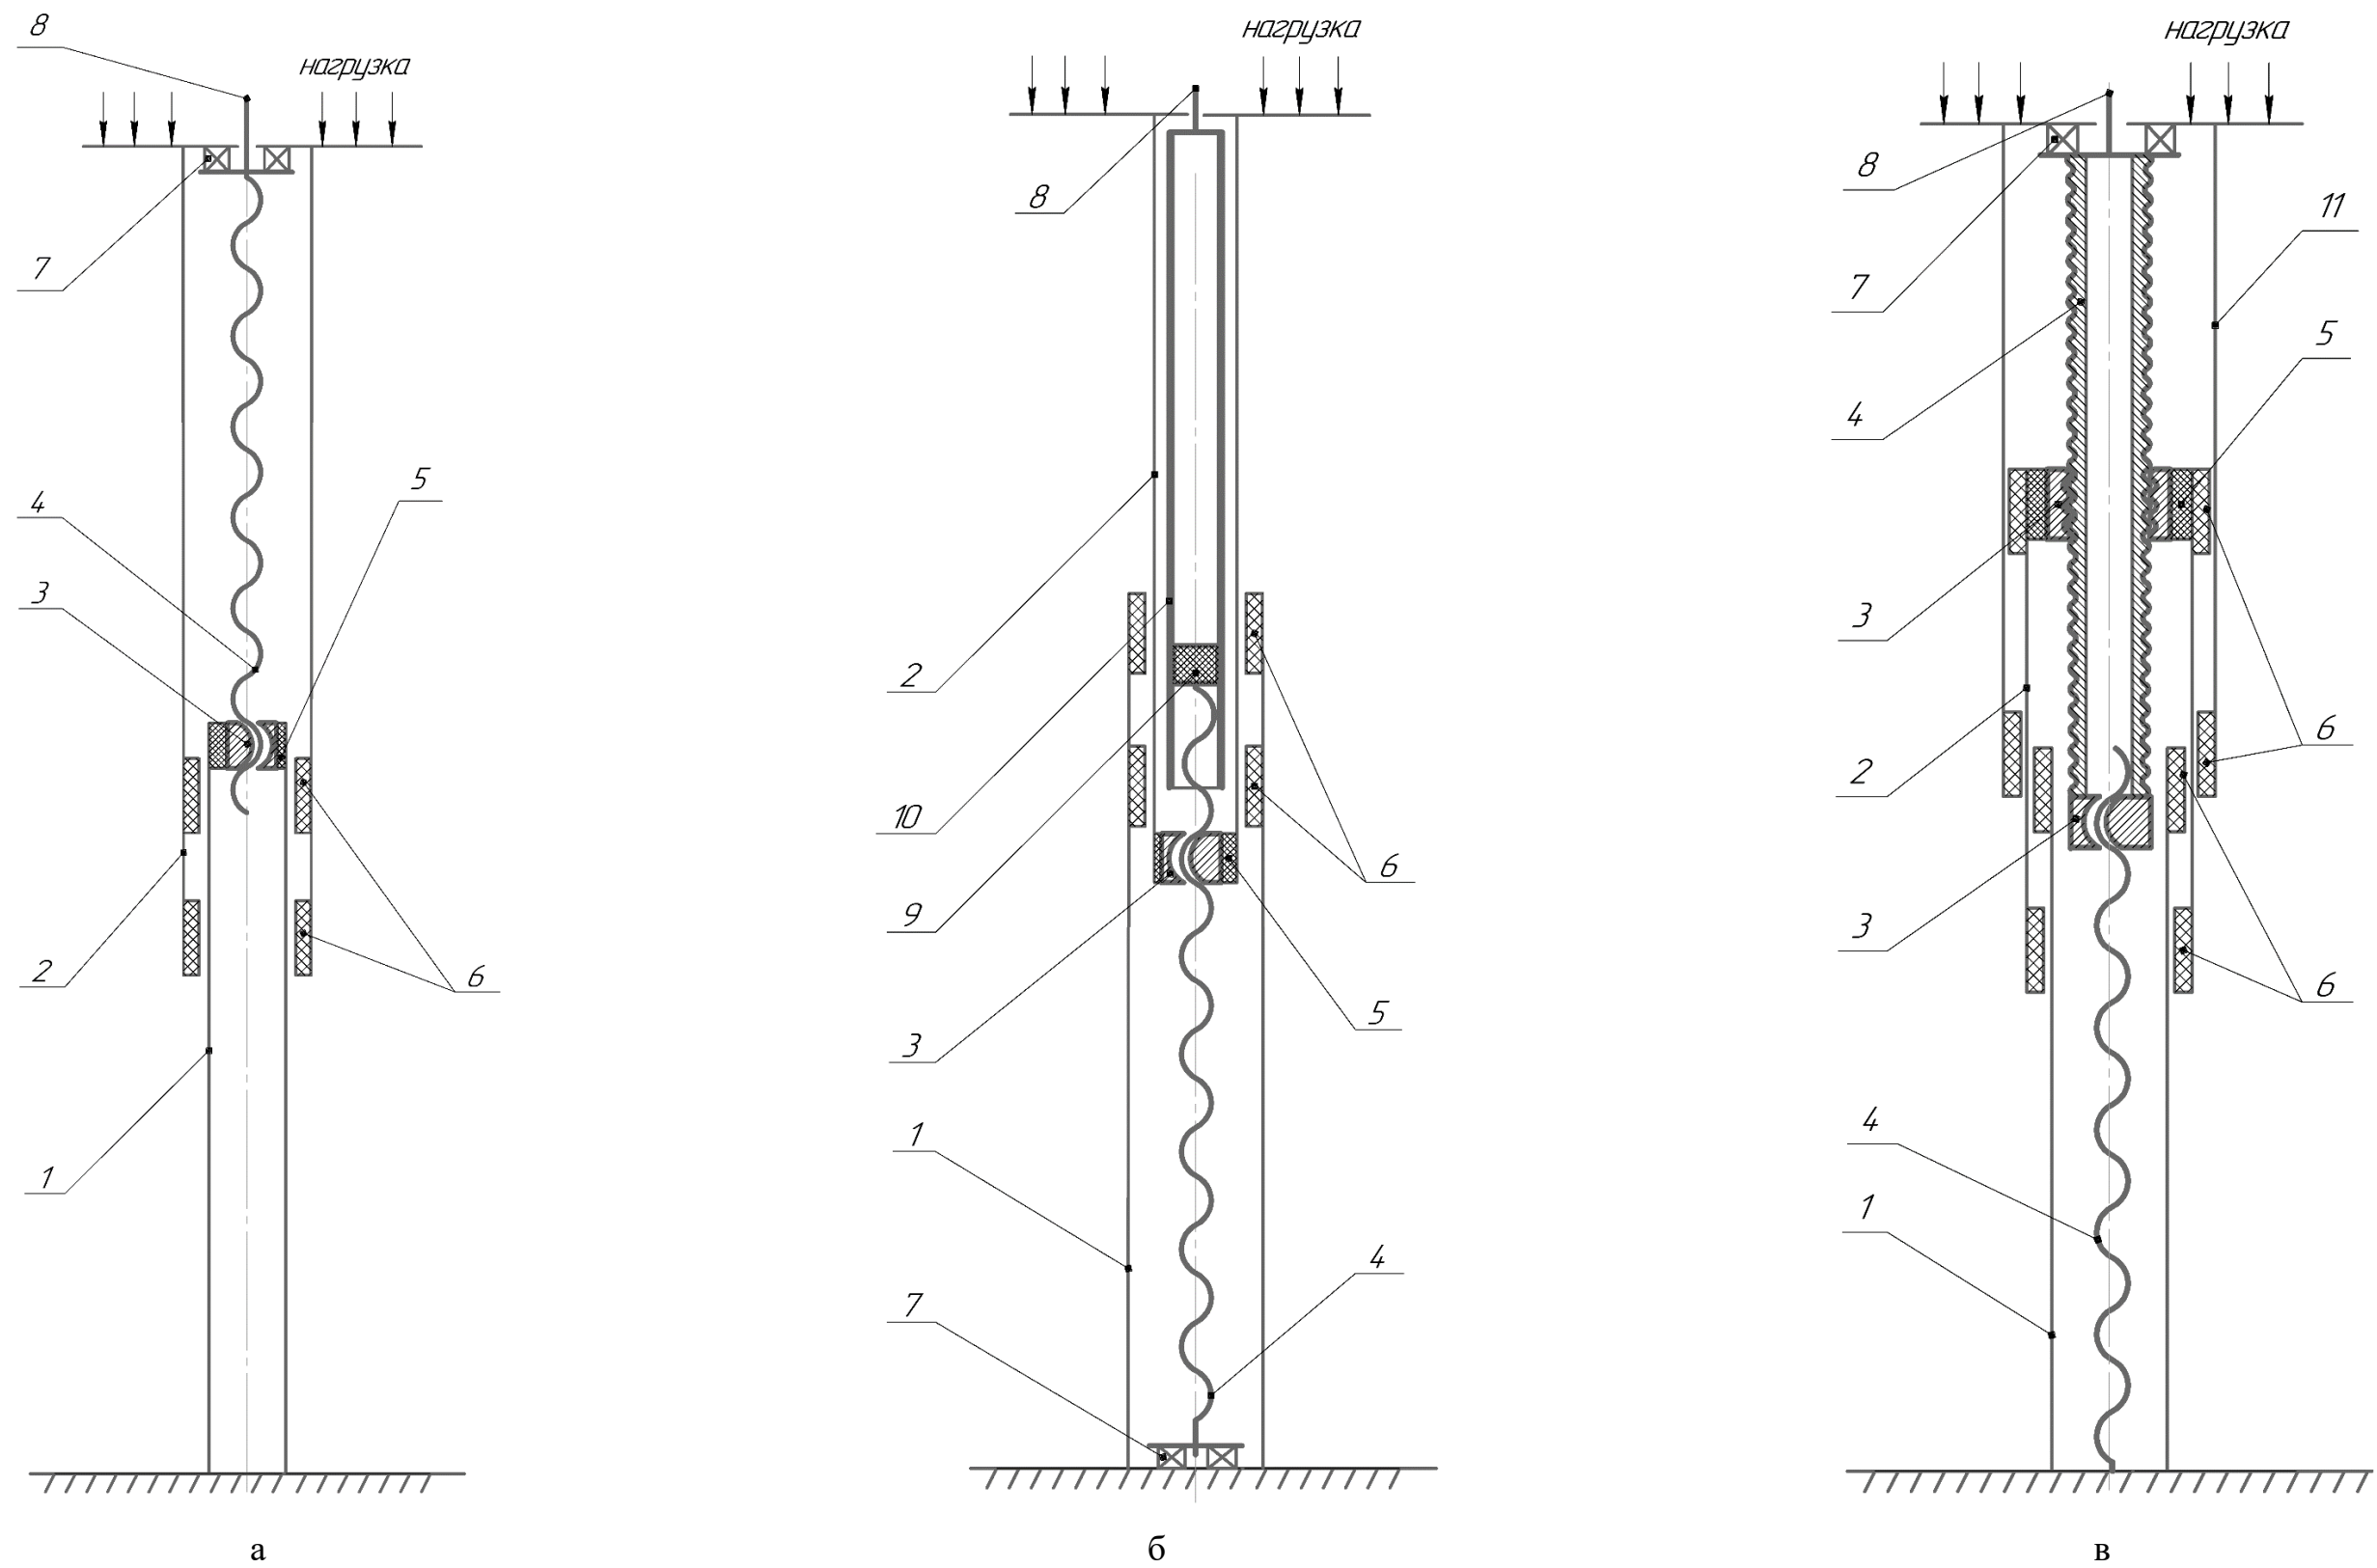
Варианты конструкций выдвжных механизмов с винтовой передачей:
